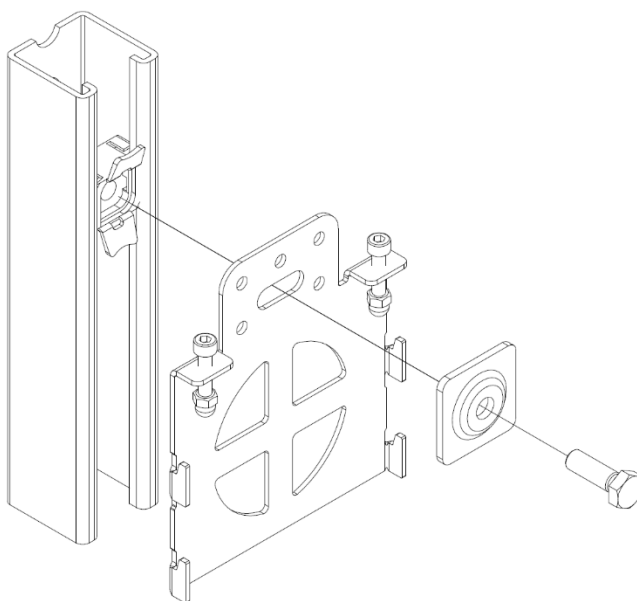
Explosionszeichnung der Teile zur Befestigung der Wandmontageplatte
